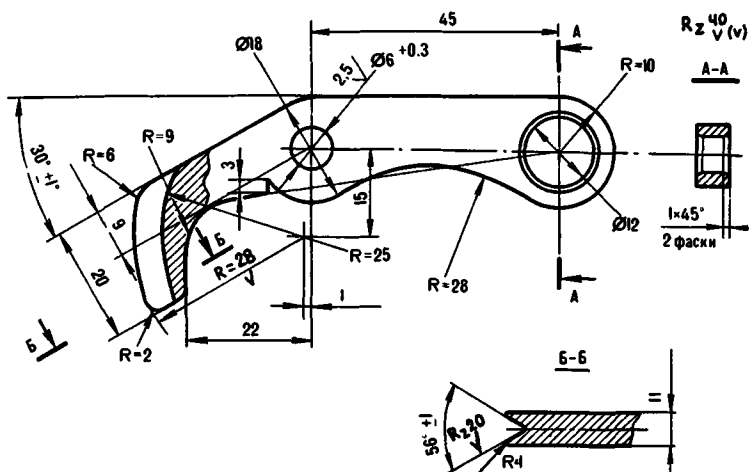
Кулачковый захим конструкции Абалакова. Рычаг
